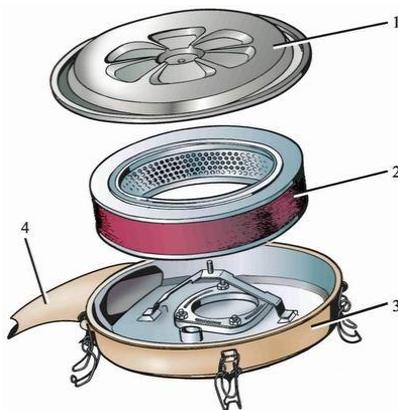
Воздушный фильтр: 1 – крышка; 2 – фильтрующий элемент; 3 – корпус; 4 – воздухозаборник
